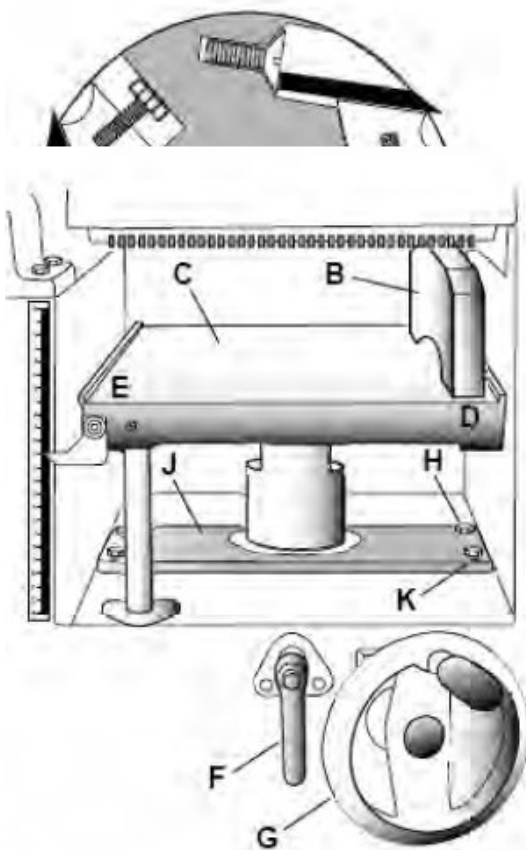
Überprüfung des Hobeltisches parallel zur Messerwelle
